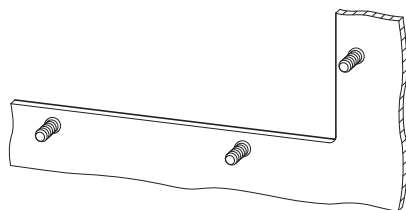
Schweiß-Gewindebolzen M4 x 12 am Blech
